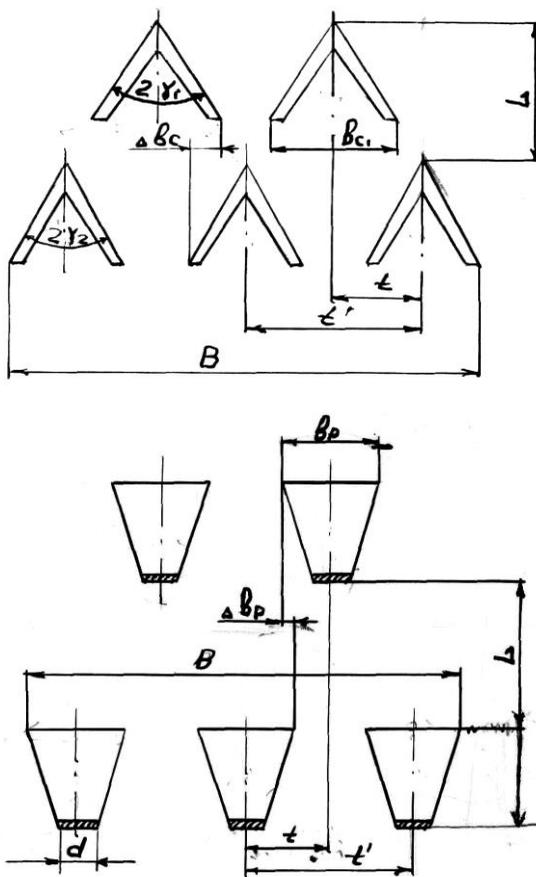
Схема расстановки стрелчатых и рыхлительных лап парового культиватора
